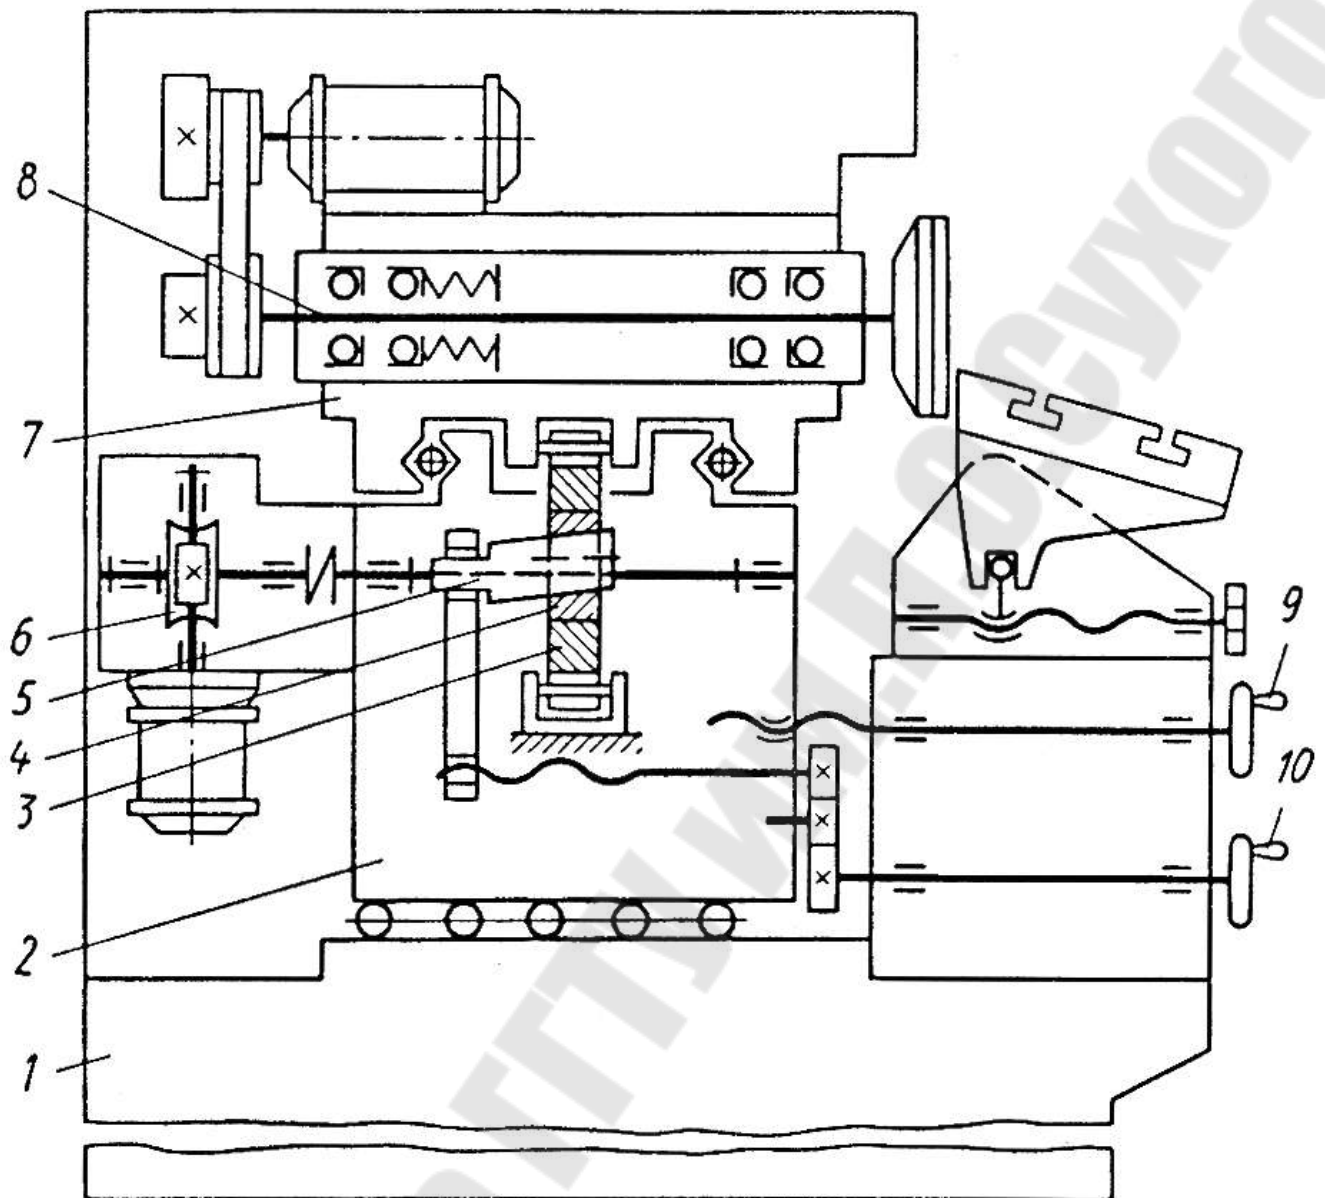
Принципиальная схема станка модели 3622 для заточки резцов:
